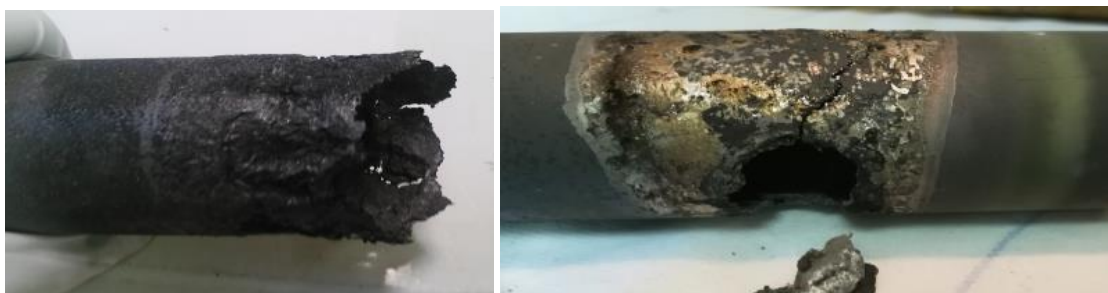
Photographies du tube de protection en INCONEL 600 endommagé après explosion de l'ampoule
